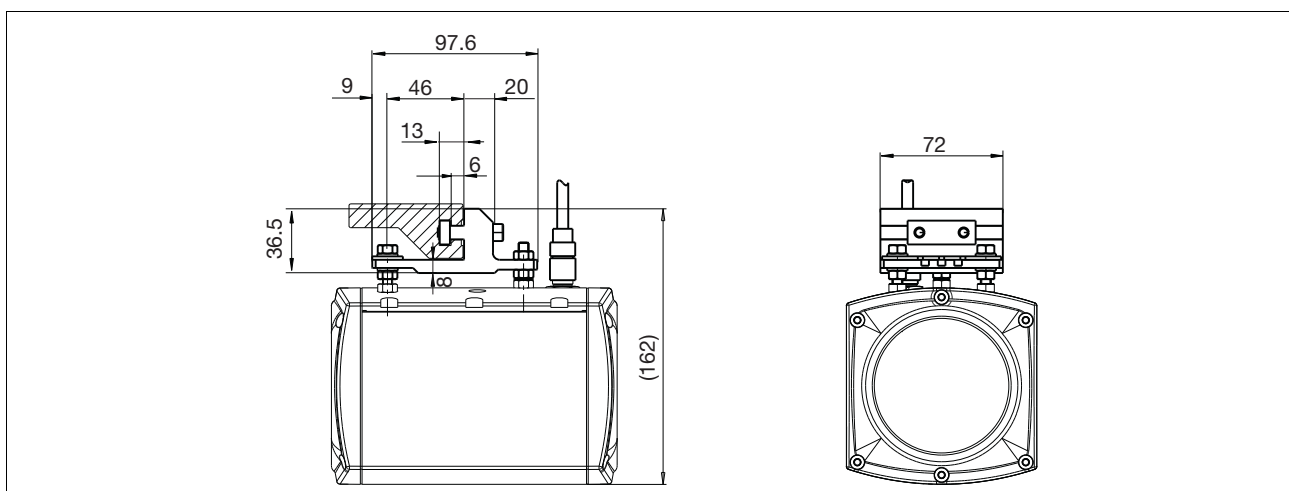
Abmessungen des Befestigungssatzes für den Sender, Maßangaben in mm
